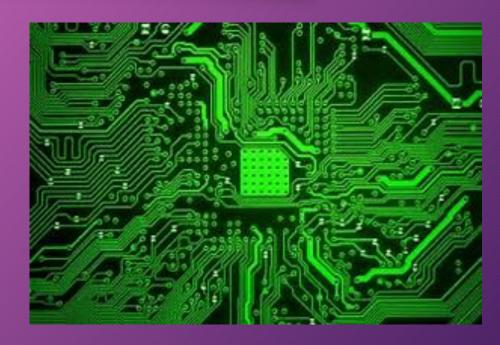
Diseño de un PCB (Se muestran principalmente las vías)
